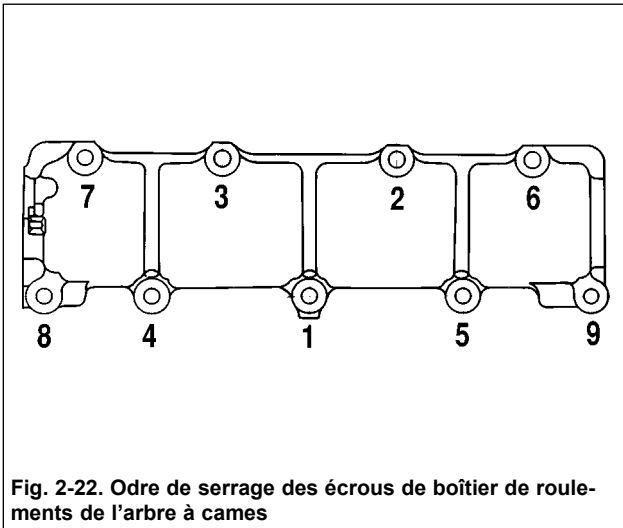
Ordre de serrage des écrous de boîtier de roulements de l'arbre à cames
